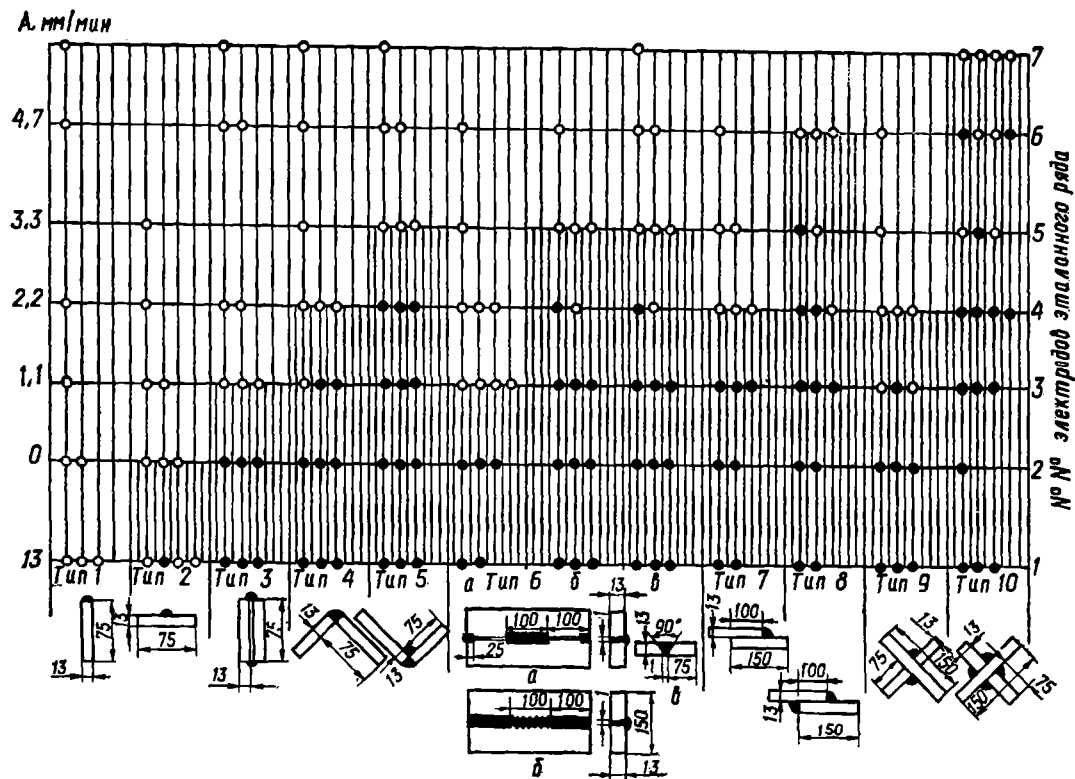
Влияние типа сварного соединения на образование горячих трещин (основной металл Ст3; режим сварки:
